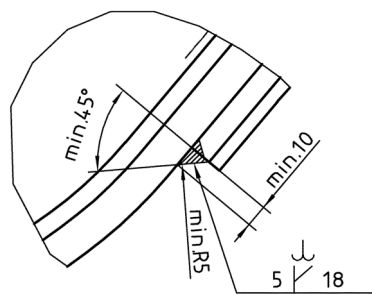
Fertigungszeichnung Detailansicht Abbinder neue Geometrie
